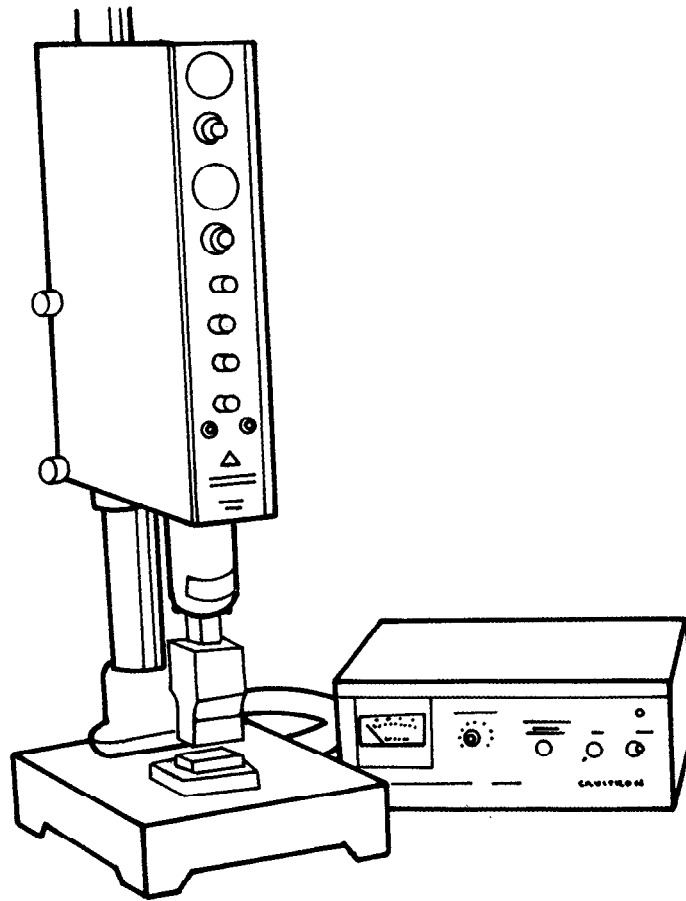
Soldadora ultrasónica de plásticos.
